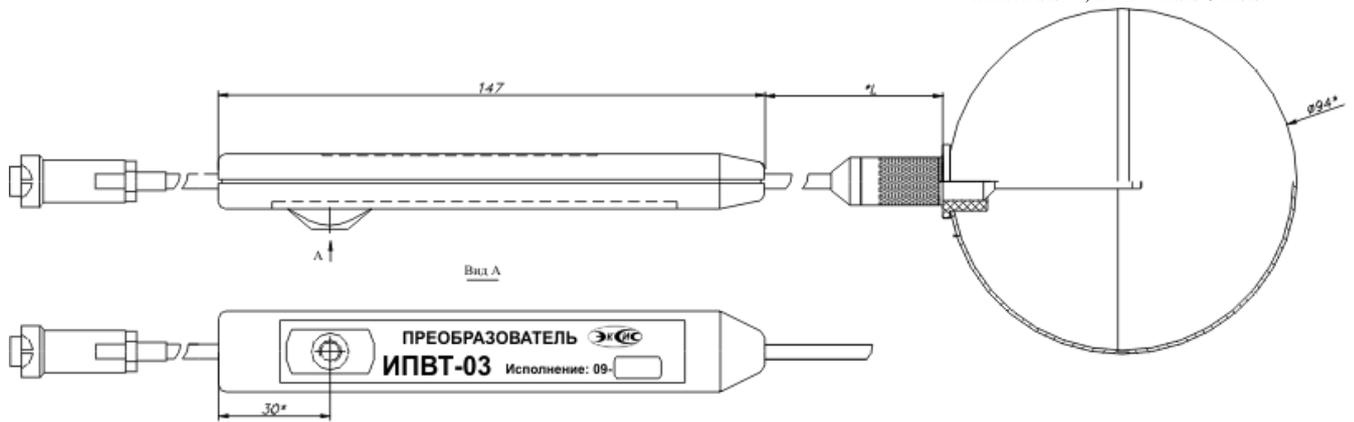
Измерительный преобразователь ИПВТ-03-09-ПВ
